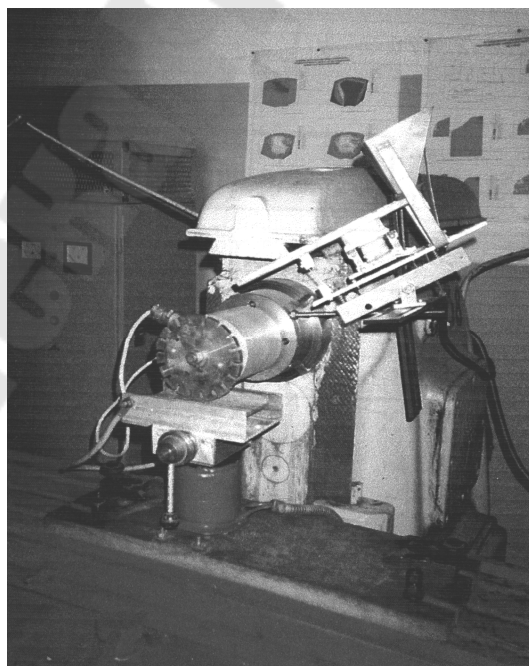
Общий вид лабораторной установки первого типа для магнитно-электрического упрочнения плоских поверхностей
